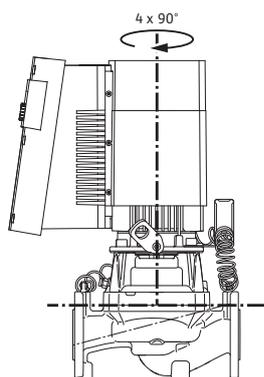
Posiciones de montaje admisibles con eje del motor vertical
